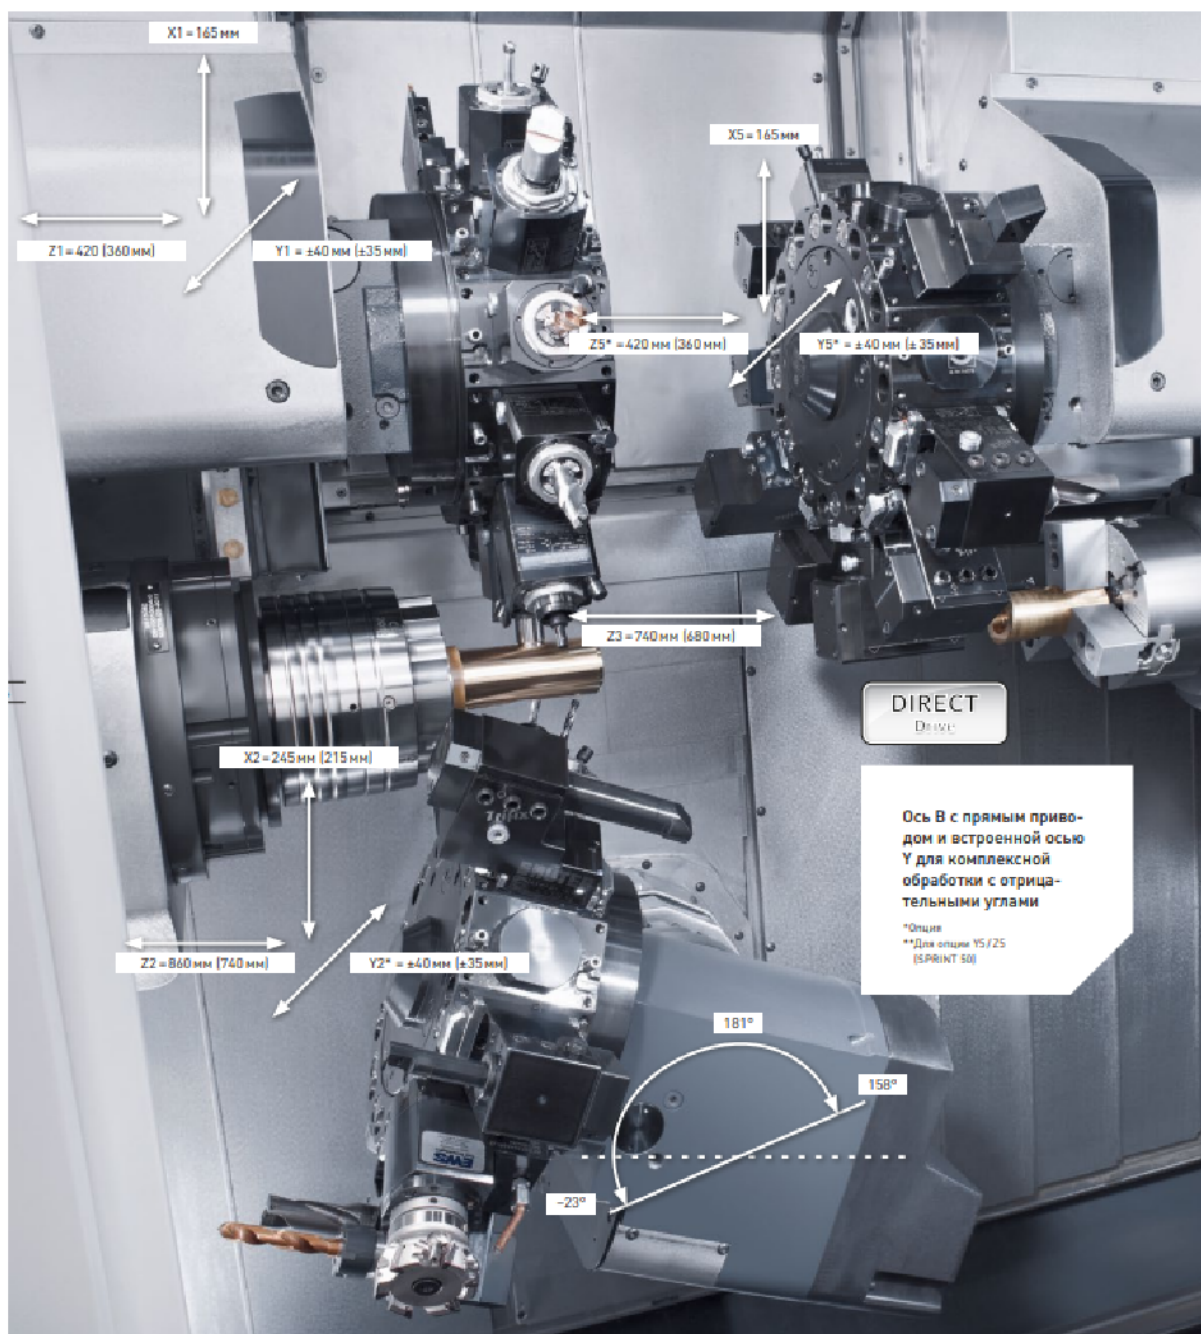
Токарно-револьверный станок с двумя шпинделями и тремя револьверными головками
